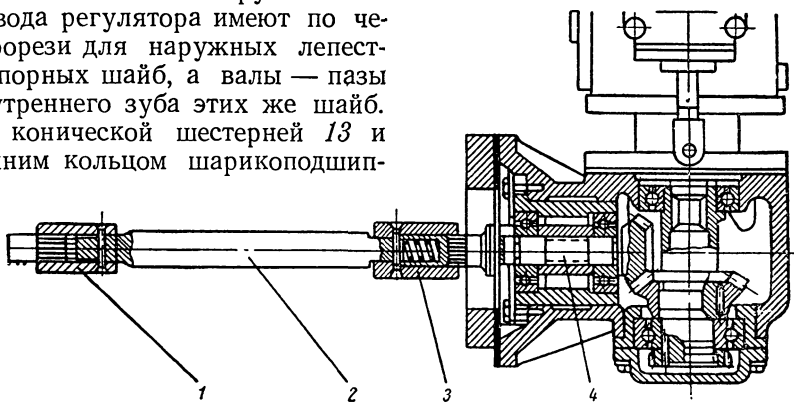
а. Привод регулятора числа оборотов (боковой):
